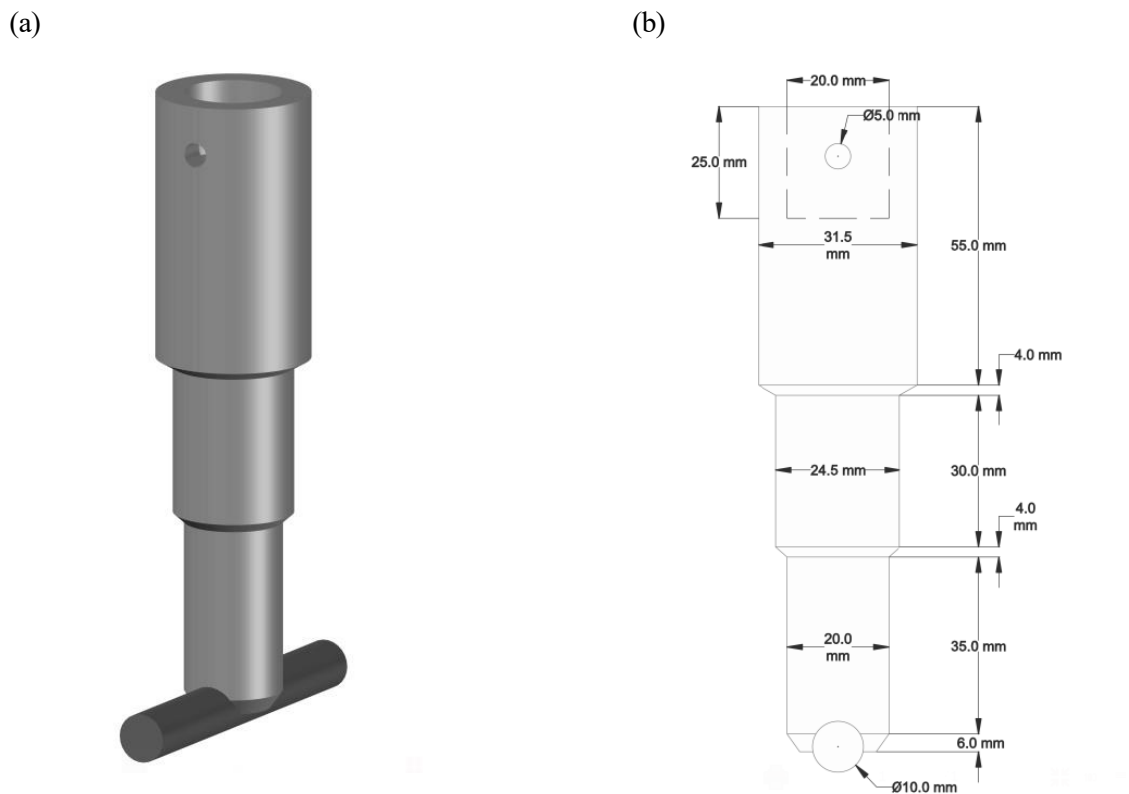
(a) Modelo 3D del útil y, (b) Corte en alzado acotado
